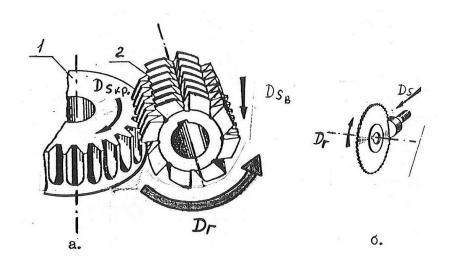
Схема нарезная зубьев методам обкатки на фрезерном станке: а — нарезание зубьев; б — прорезание паза дисковой фрезой; 1— заготовка; 2 — червячная фреза
